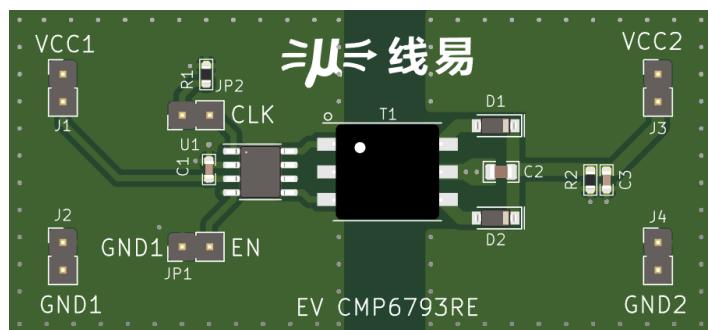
PCB 示意图(尺寸: 30x 65mm)
